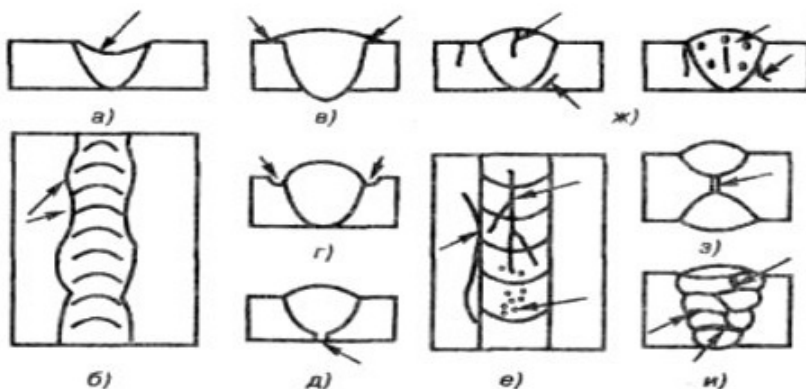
Виды дефектов сварных соединений (где а — ослабление шва, б — неравномерность ширины, в — наплыв, г — подрез, д — непровар, е — трещины и поры, ж — внутренние трещины и поры, з — внутренний непровар, и — шлаковые включения).
